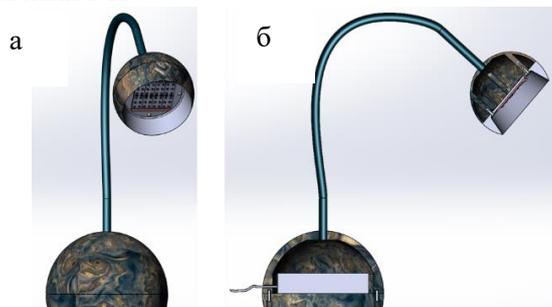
Внешний вид (а) и вид в разрезе (б) настольного светильника
